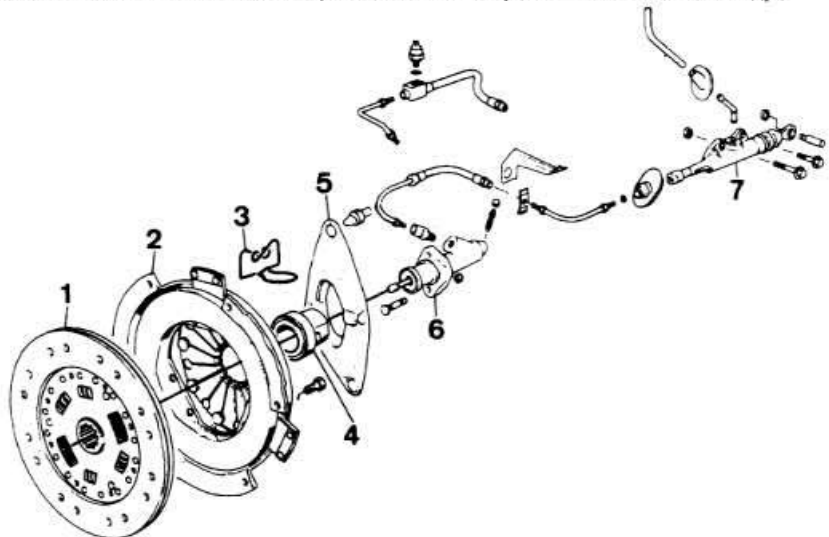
Детали сцепления и гидропривода сцепления автомобилей с дизельным двигателем:
